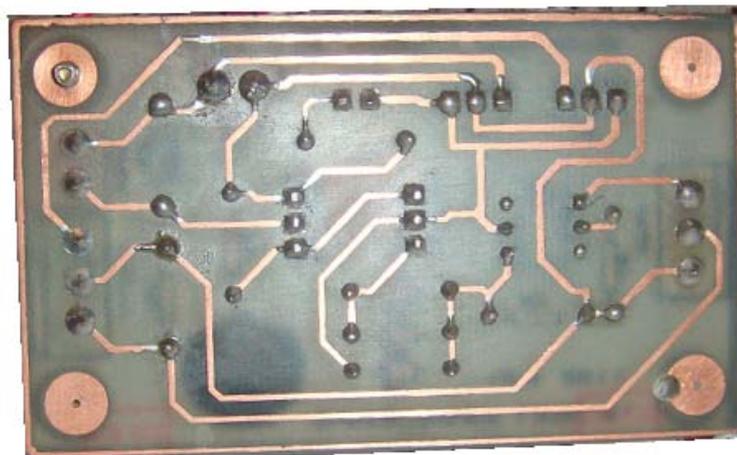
PISTAS Y SOLDADURA DE LA PLACA DE INTERFAZ FPGA-MOTOR DC.
